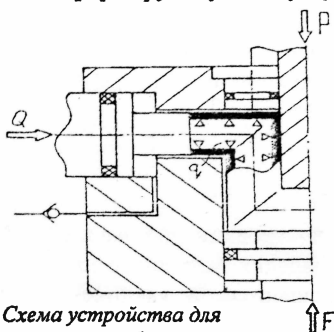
Схема устройства для деформирования трубной заготовки в режиме жидкостного трения между поверхностями заготовки и матрицы
